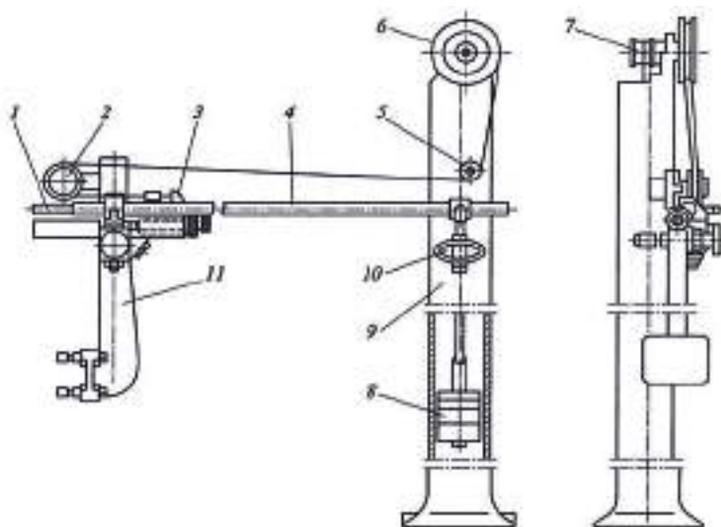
Схема механизма подачи прутка с помощью груза: 1 – толкатель; 2, 5 – ролики; 3 – флажок; 4 – направляющая труба; 6, 7 – шкивы; 8 – груз; 9 – колонка; 10, 11 – кронштейн
